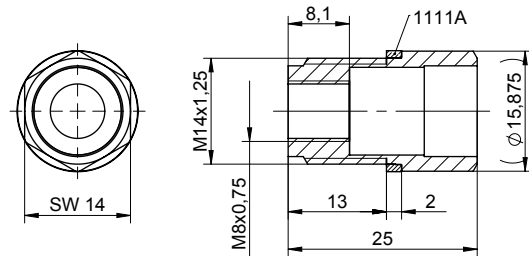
Adapter Typ 6589Q01. Sensor frontbündig
